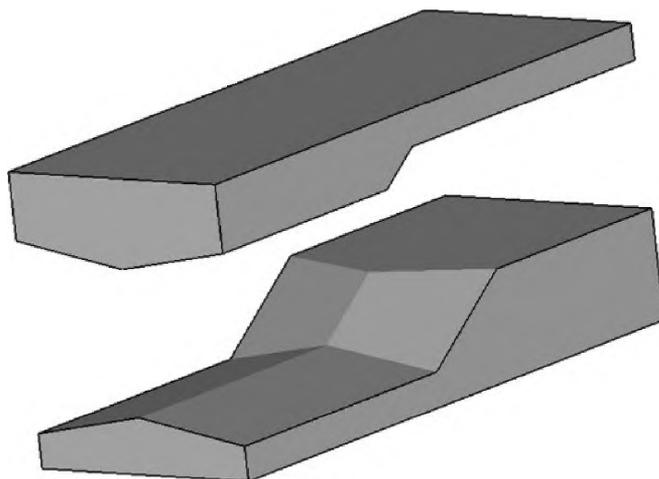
Новая конструкция ступенчато-клиновых бойков
